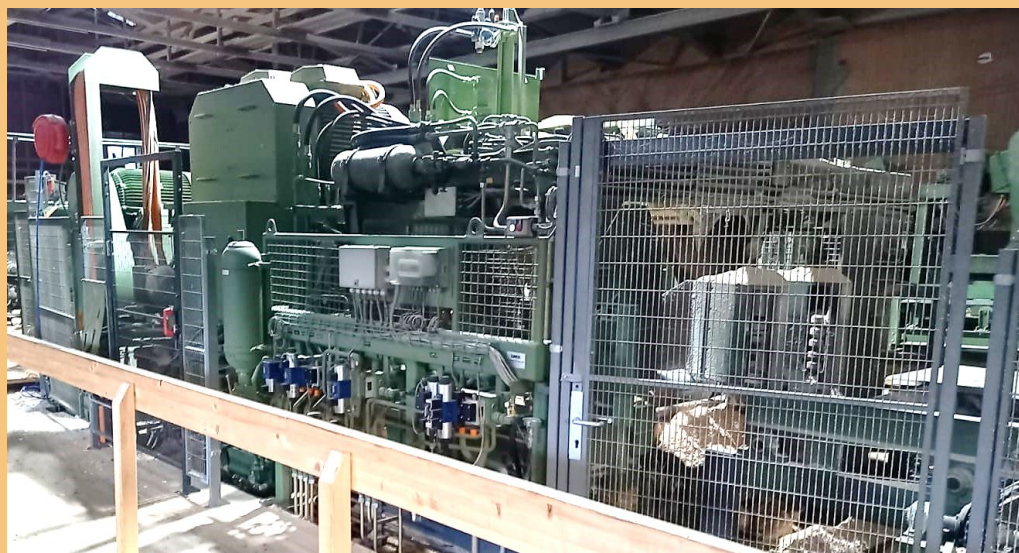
installations hydrauliques d'une machine principale (source : P. Schmider, Schilliger AG)
